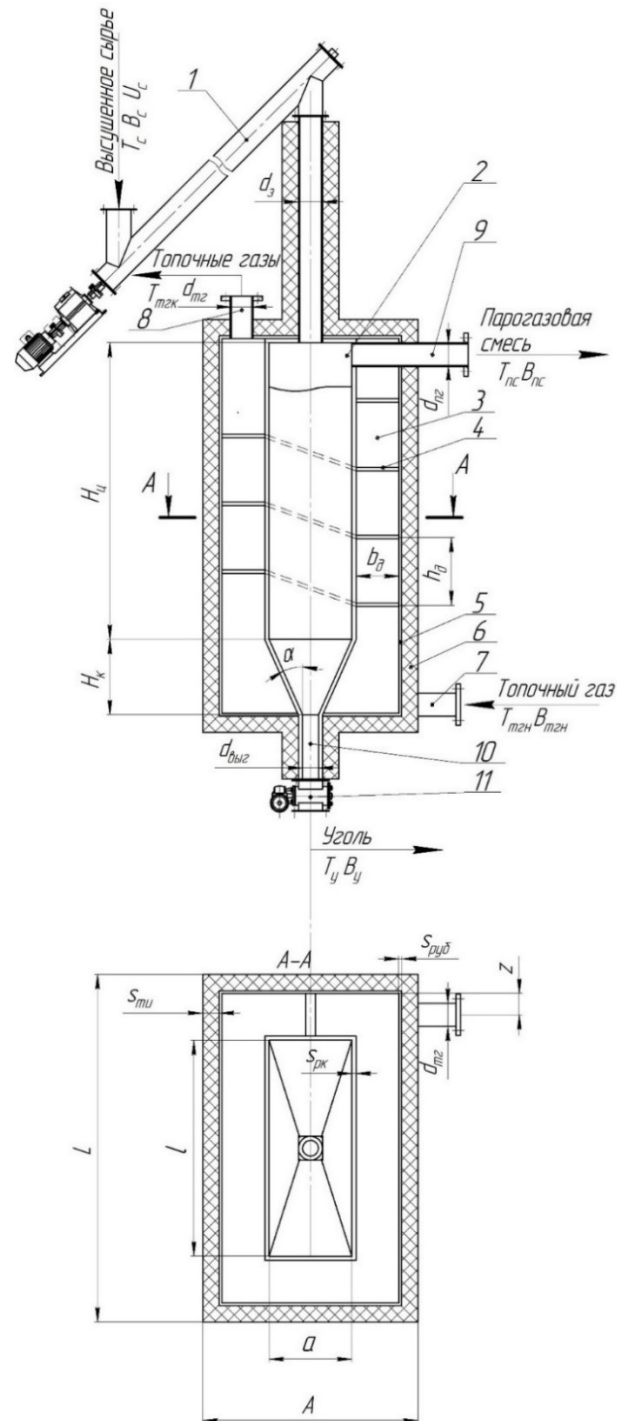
Схема камеры пиролиза: 1 – шнековый транспортёр; 2 – реакционная камера; 3 – спиральный дымоход; 4 – спиральные направляющие; 5 – рубашка; 6 – теплоизоляция; 7 – патрубок подачи топочного газа в рубашку; 8 – патрубок отвода топочного газа из рубашки; 9 – патрубок удаления пиролизного газа; 10 – патрубок выгрузки угля; 11 – шлюзовый питатель
